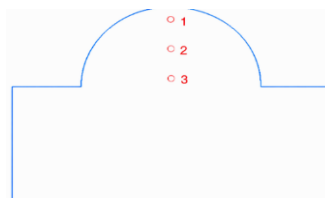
Схема точек для измерения твердости наплавленного образца
